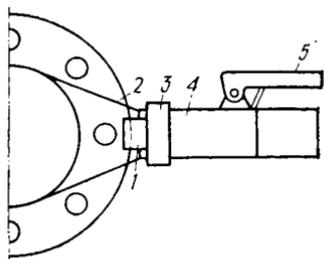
Гидравлическое приспособление для раздвижки фланцев:
